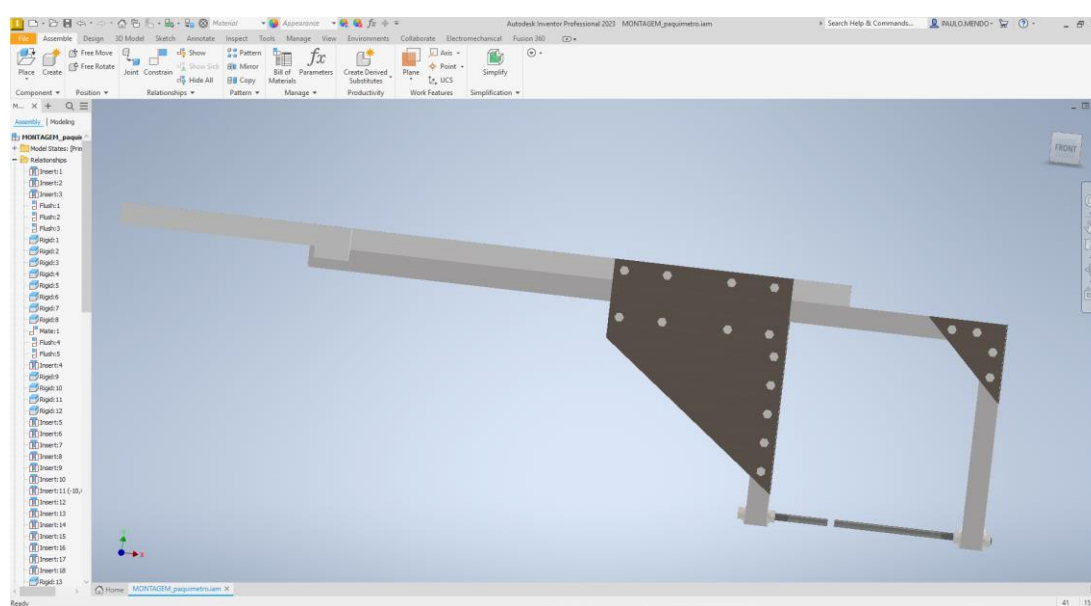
Desenho CAD do paquímetro, in Autodesk Inventor
